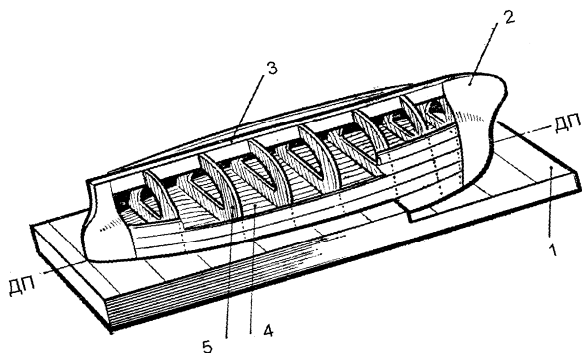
Виготовлення набірного корпусу моделі бота:
